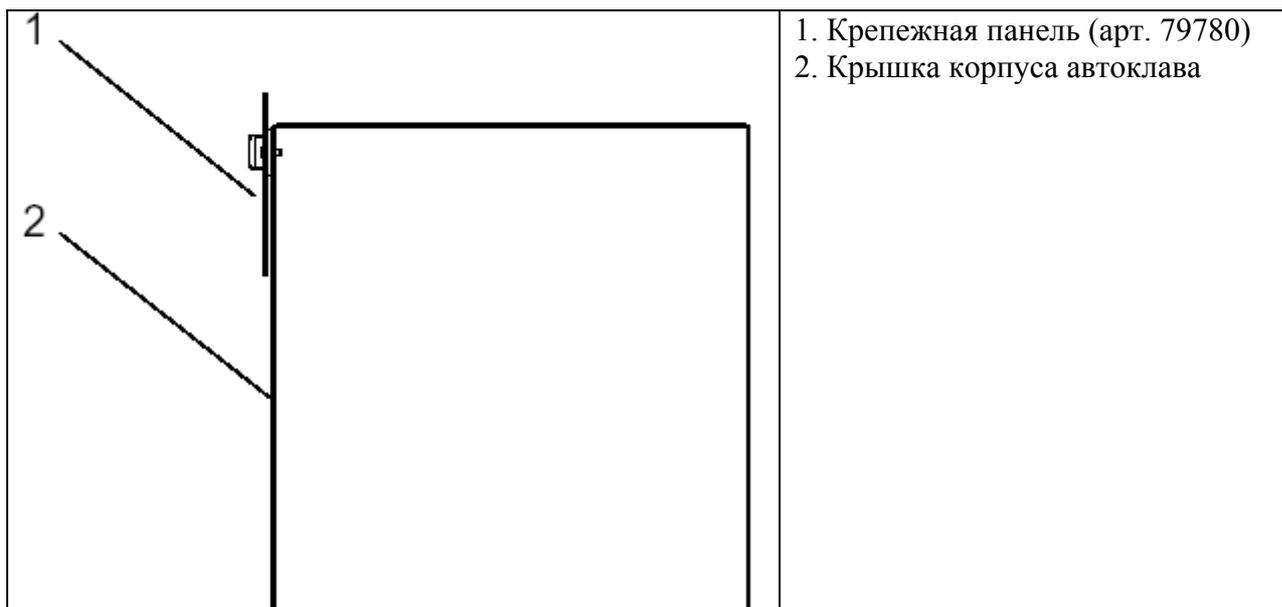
Крепление к корпусу с помощью крепежных приспособлений и окончательное положение крепежной панели
